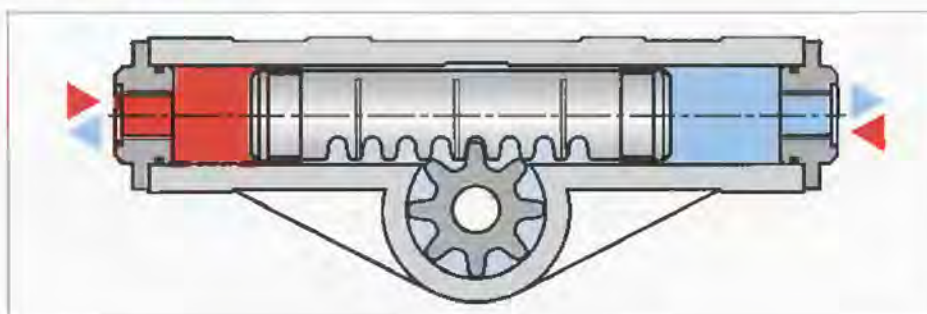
Поворотный гидродвигатель с гидроцилиндром, шестеренно-реечным приводом и поршнем, совершающим возвратно-поступательное движение
